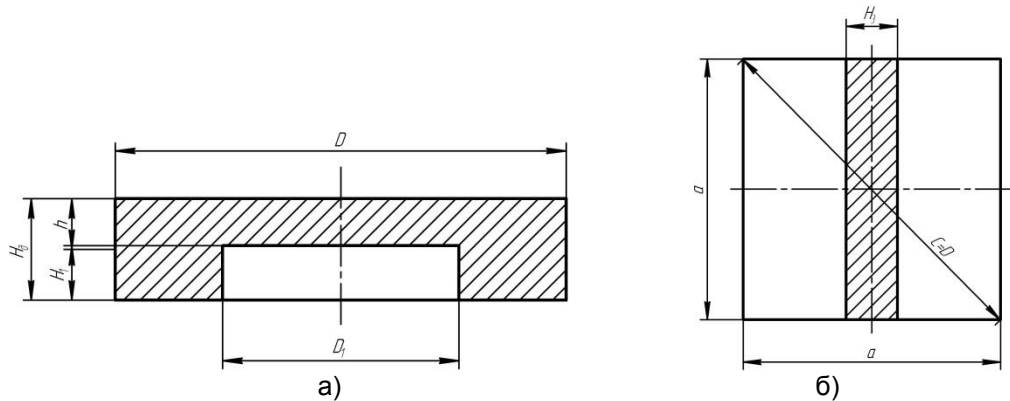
Вихідні параметри готової деталі (а) заготовки (б)
